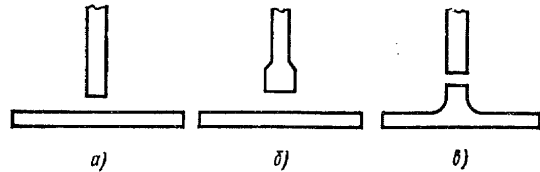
Схемы подготовки кромок под соединение стенки балки с полкой
